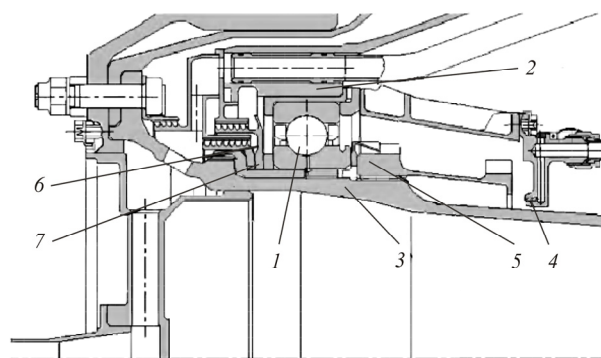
Подача масла через внутреннее кольцо подшипника: 1 – радиально-упорный подшипник; 2 – корпус; 3 – вал ротора; 4 – форсунка; 5 – втулка; 6, 7 – лабиринты
